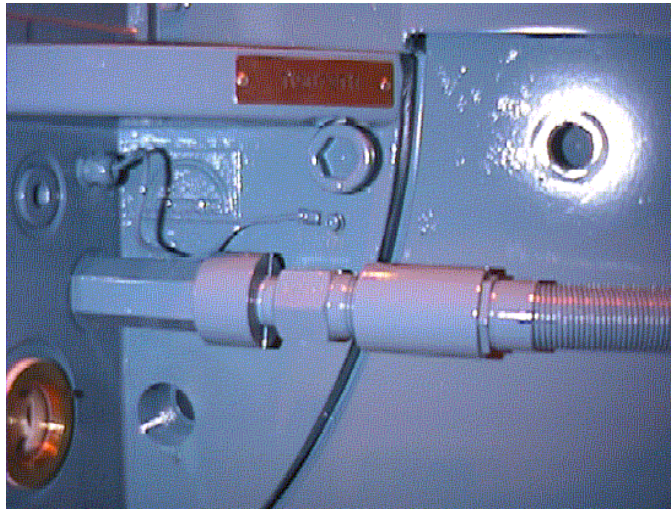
Кабель заземления подшипника приводного конца (D)
